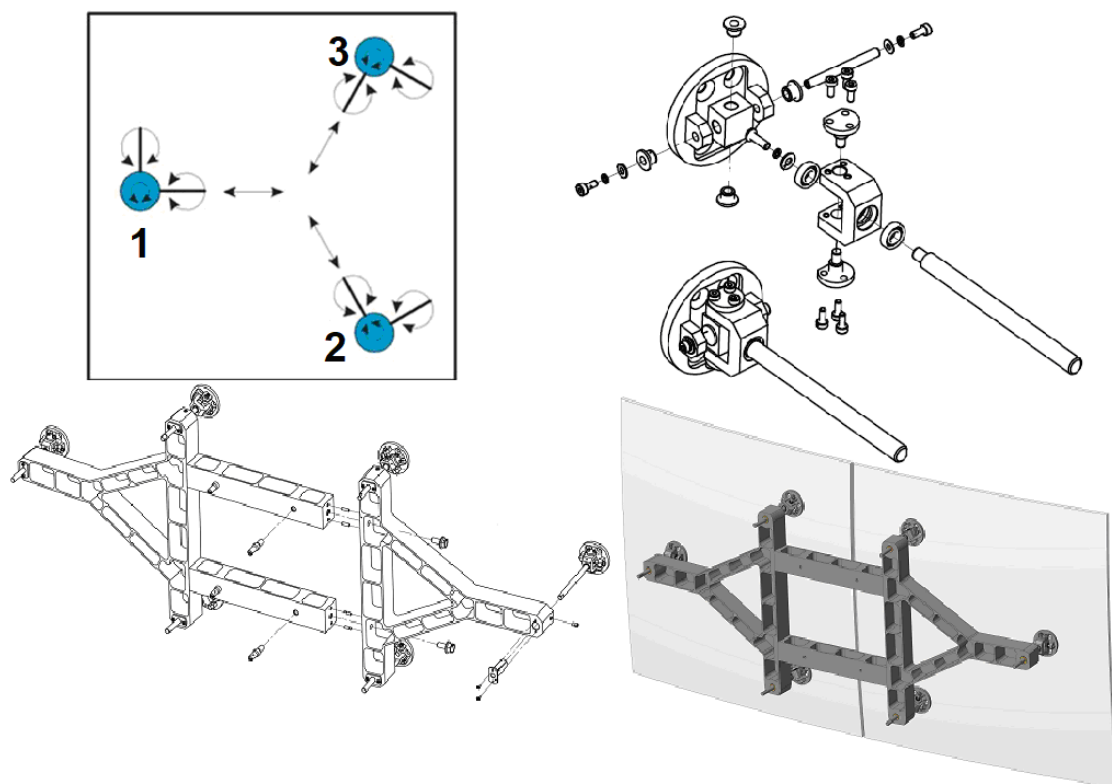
Система поддержки зеркальных плиток: схема 3-х точечного крепления зеркала (слева вверху); механизм поддержки и юстировки зеркал (справа вверху); конструкция рамки крепления 2-х плиток (слева внизу), рамка с установленными двумя зеркальными плитками (справа внизу)
